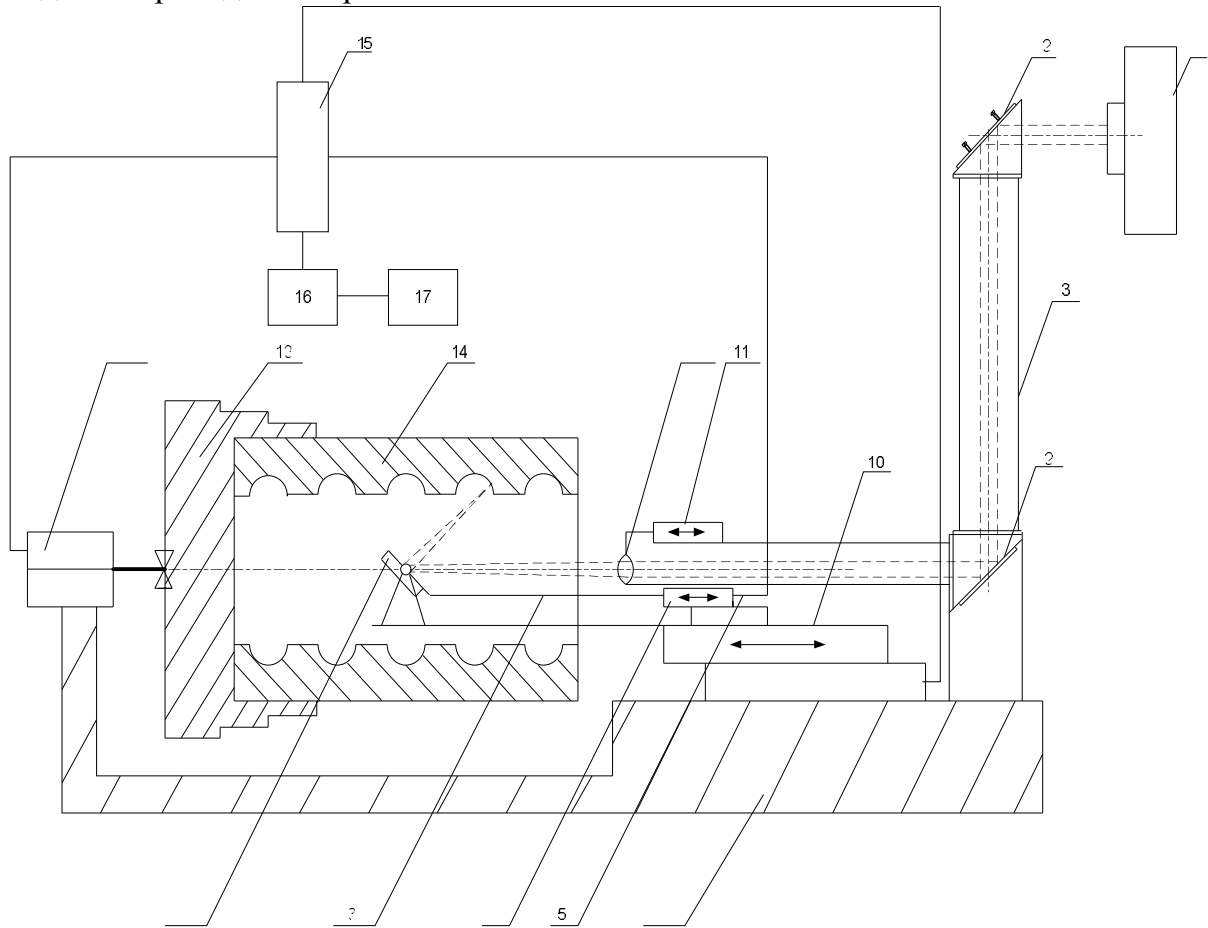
Лазерное устройство для обработки внутренней поверхности изделий
